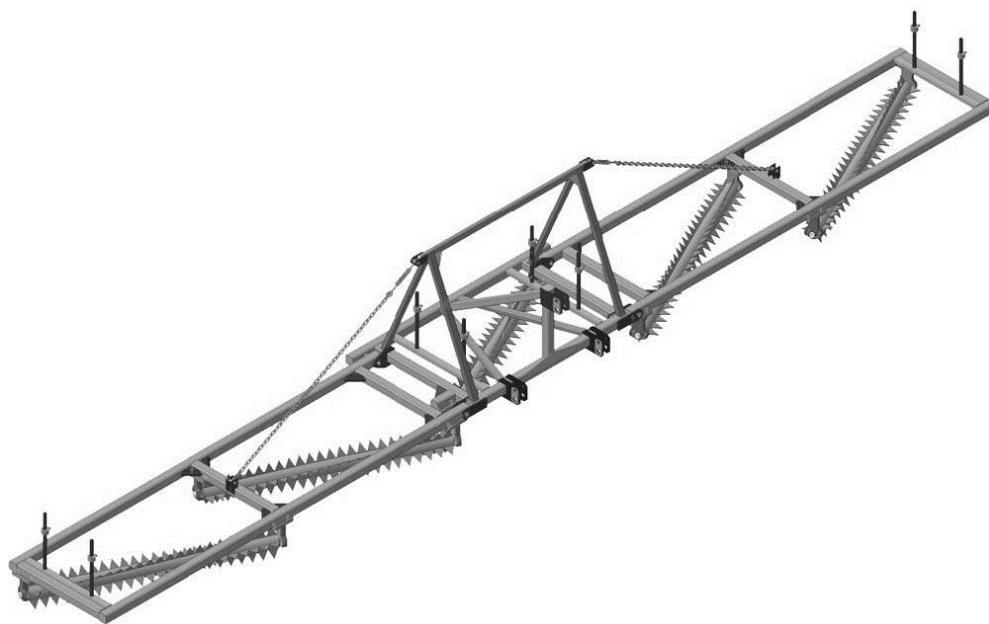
Фрезер пассивного типа ФПТ-09 конструкции ООО «Гринмаш».
